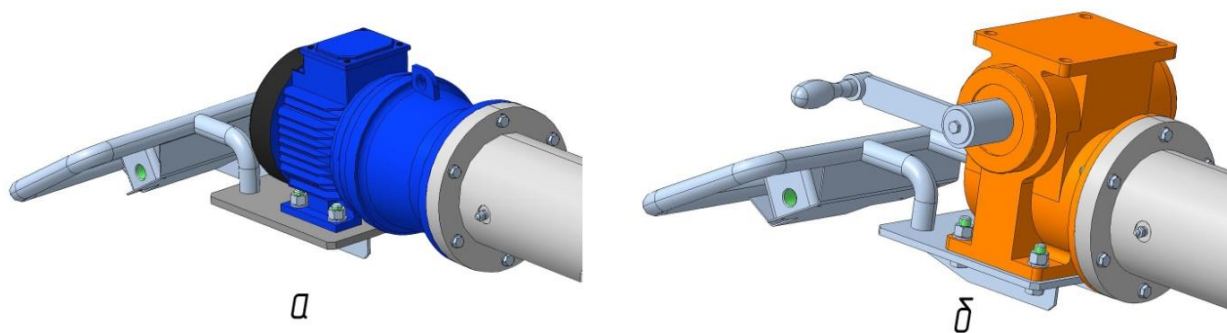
Модернізація приводу для обертання стріли: а – розроблений варіант; б – початковий варіант
